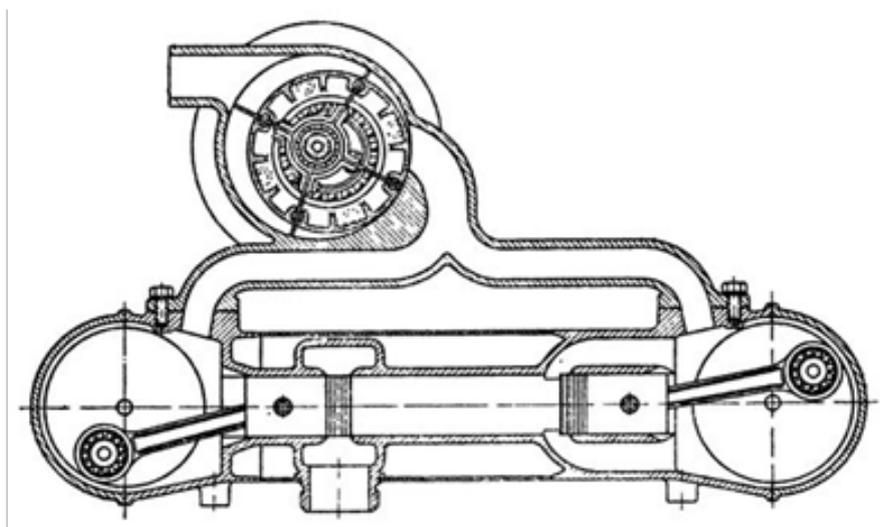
Двигатель с противоположно-движущимися поршнями с кривошипно-камерной продувкой
